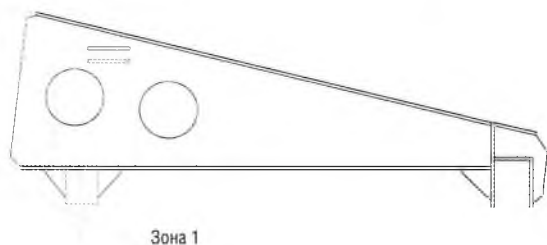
Поперечная балка выносной опоры группы кранов КС-6973
